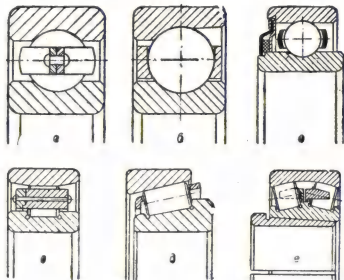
Типы подшипников качения в разрезе: а — шариковый радиальный однорядный; б — шариковый радиальноупорный однорядный; в — шариковый радиальный однорядный с односторонним уплотнением; г — роликовый с короткими цилиндрич. роликами; д — роликовый радиальноупорный с конич. роликами; е — роликовый сферический с бочкообразными роликами на закрепительной втулке.
